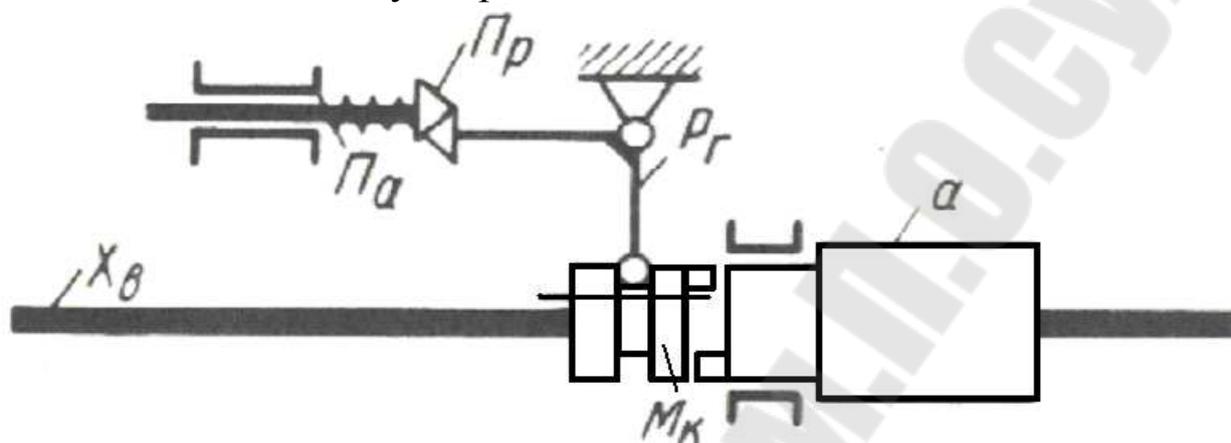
Схема самовыключающейся кулачковой муфты
